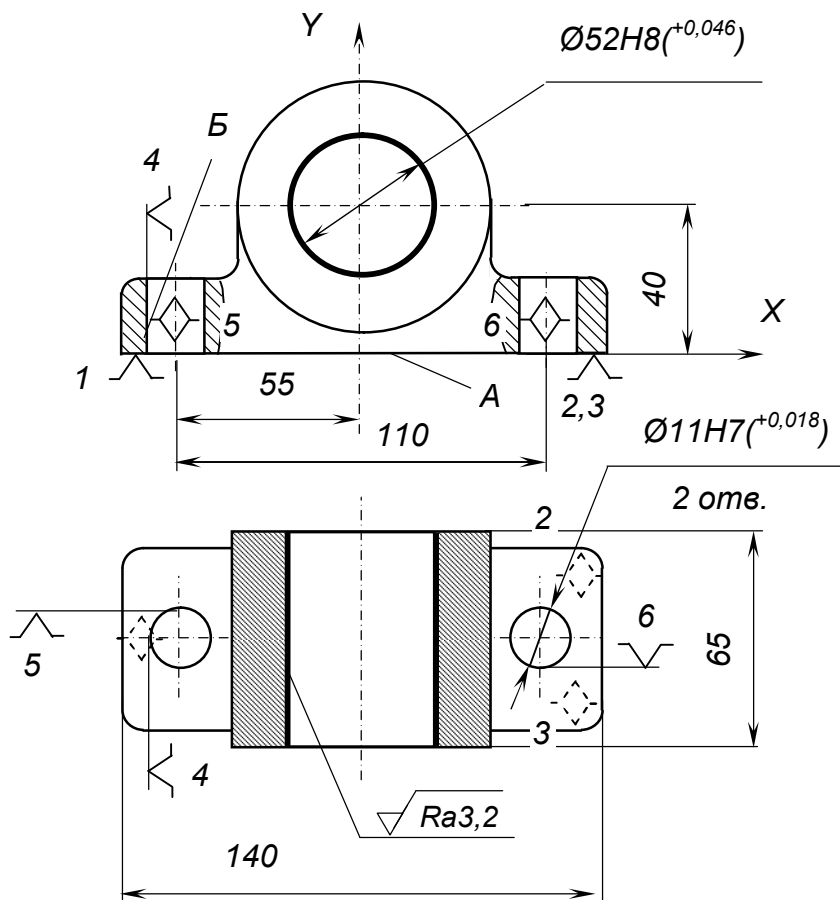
Ескіз зі схемою базування на операції обробки отвору в деталі типу «корпус»
